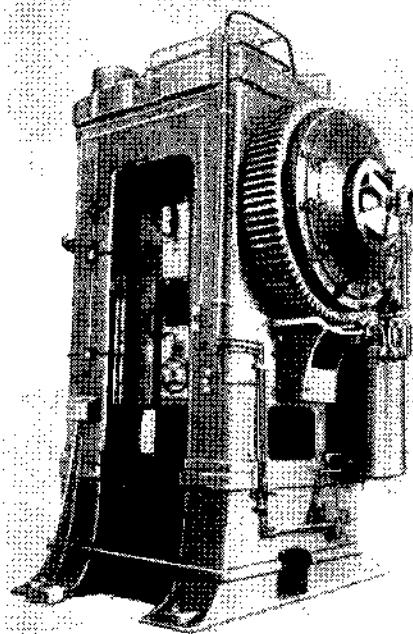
Общий вид кривошипного горячештамповочного прессы усилием 1600 *т* (16 *Мн*)
